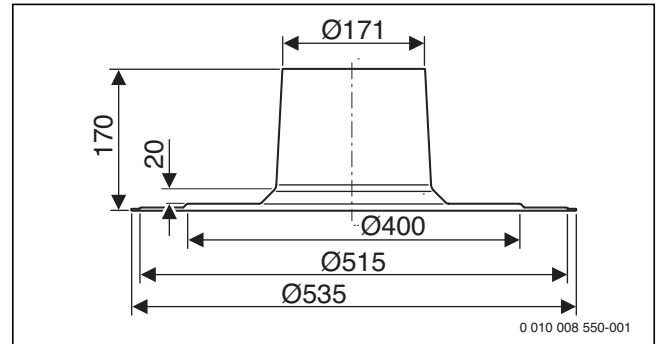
Flachdach-Klebeflansch für DN 110/160 (Maße in mm)
